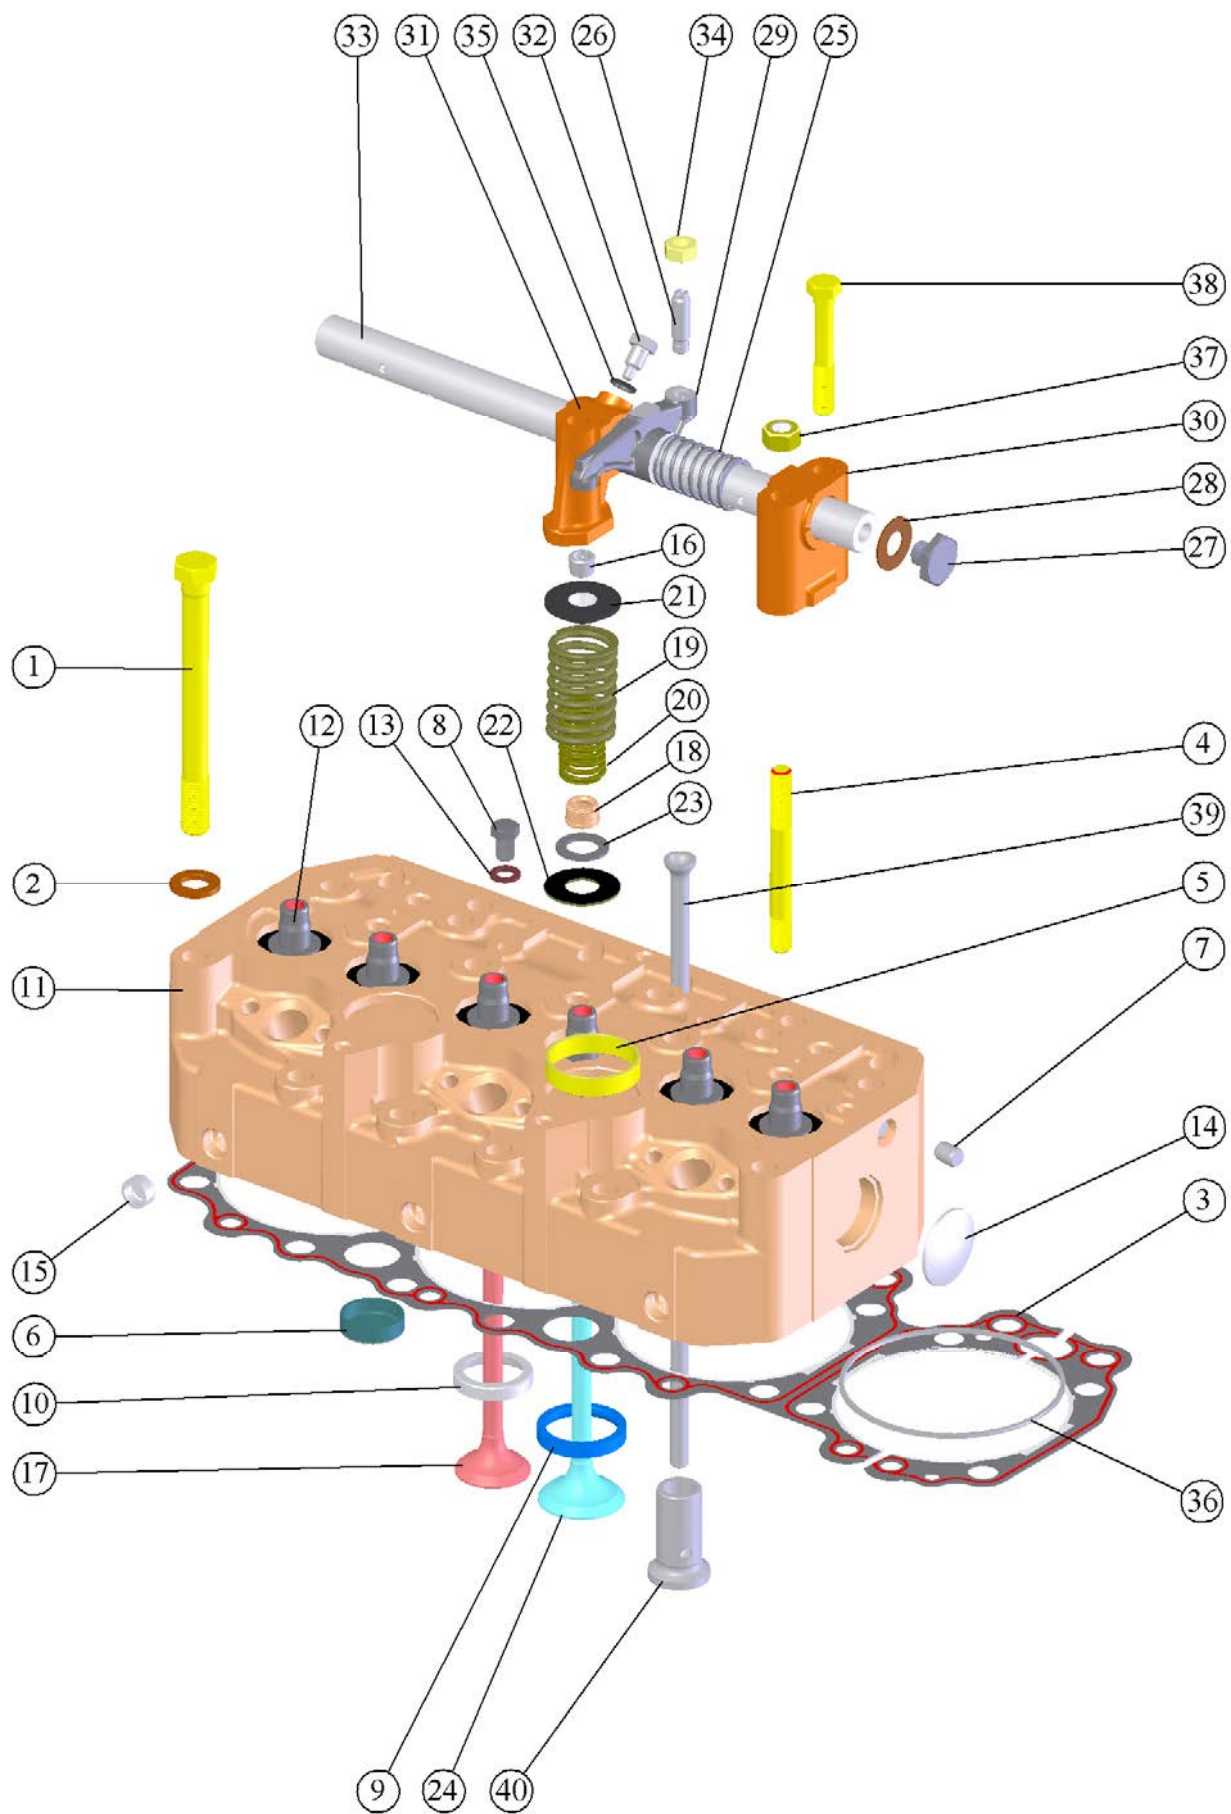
Головка цилиндров. Клапаны и толкатели клапанов.
